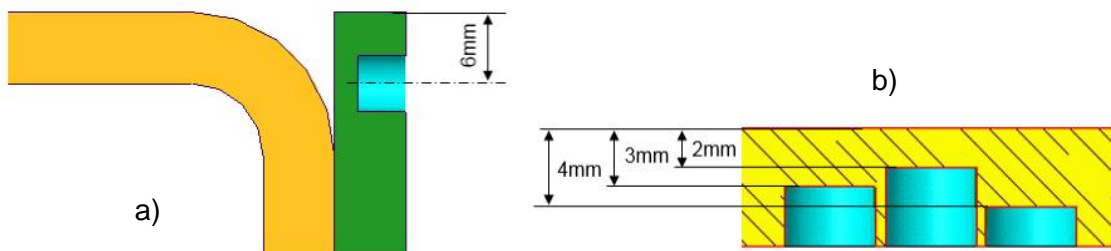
Dimensiones de barrenos para vainas, a) distancia desde la cara superior de la pieza; b) profundidad de perforaciones.
